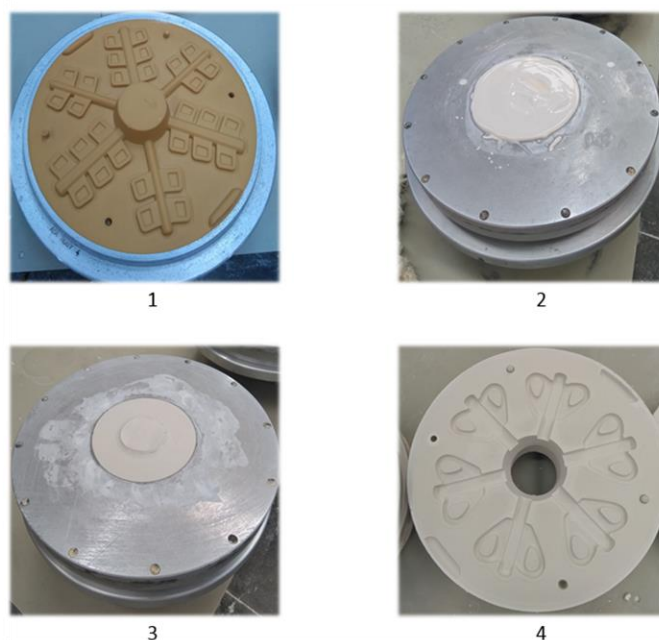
Processo de criação de um molde (da madre até ao molde).
